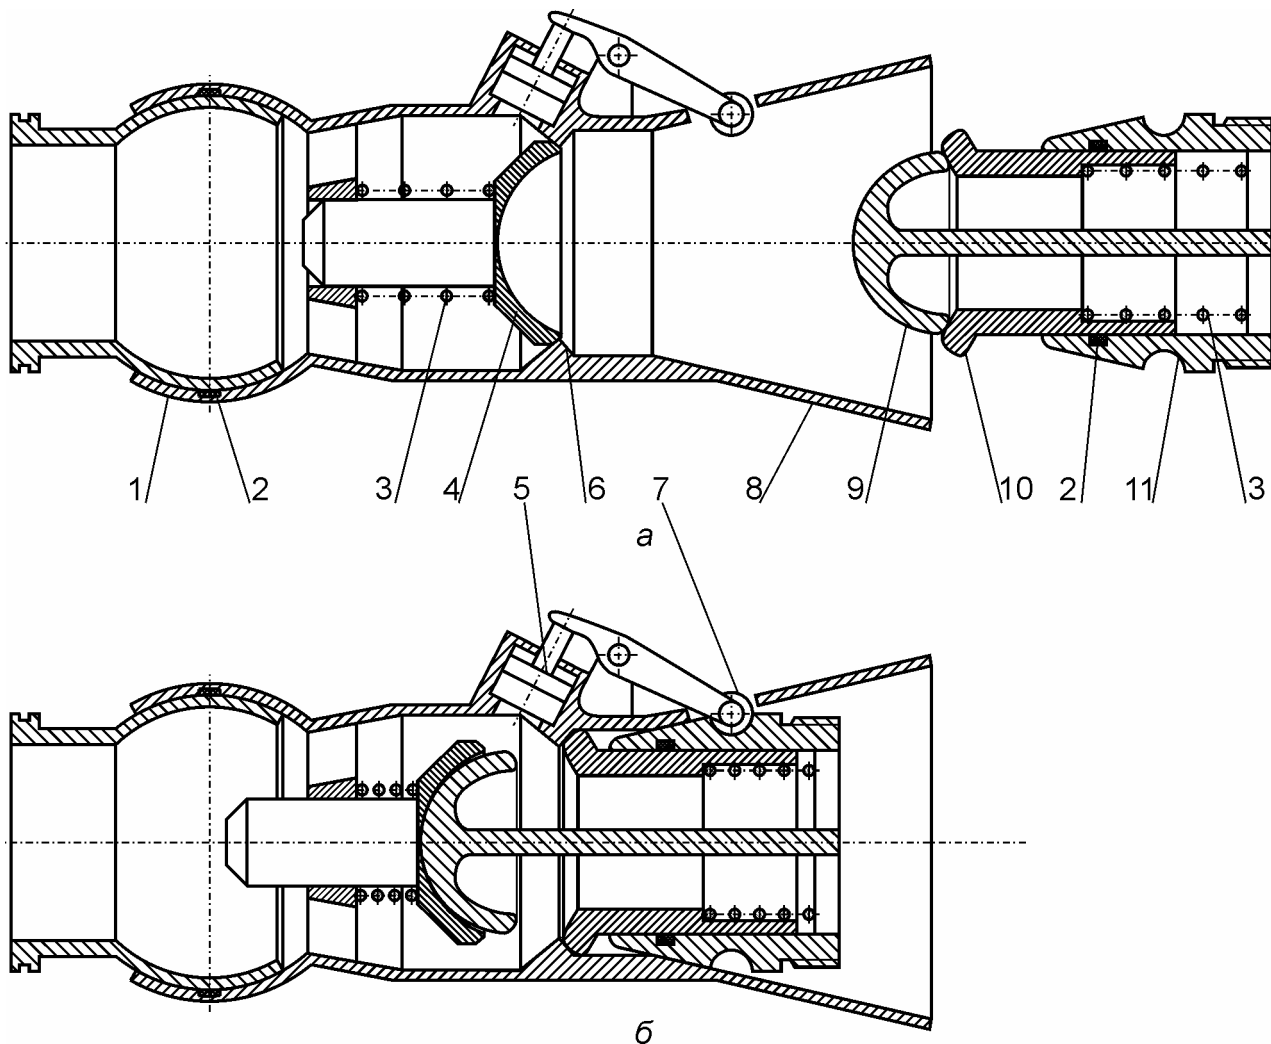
Конструкція приймального вузла та конуса-датчика (МА-2, -3, -4):
